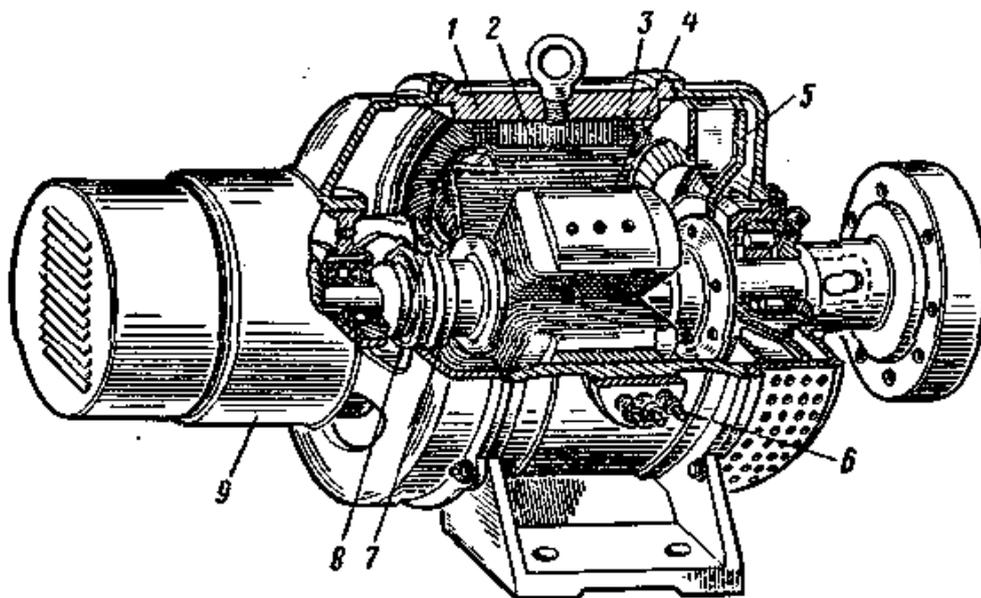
Устройство явнополюсной машины: 1 – корпус; 2 – сердечник статора; 3 – обмотка статора; 4 – ротор; 5 – вентилятор; 6 – выводы обмоток; 7 – контактные кольца; 8 – щетки; 9 – возбудитель
